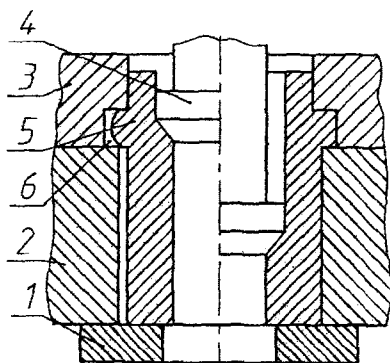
Штамповка детали с фланцем из трубной заготовки: 1 – опорное кольцо; 2 – нижняя полуформа; 3 – верхняя полуформа; 4 – пуансон; 5 – заготовка; 6 – кольцевой паз
